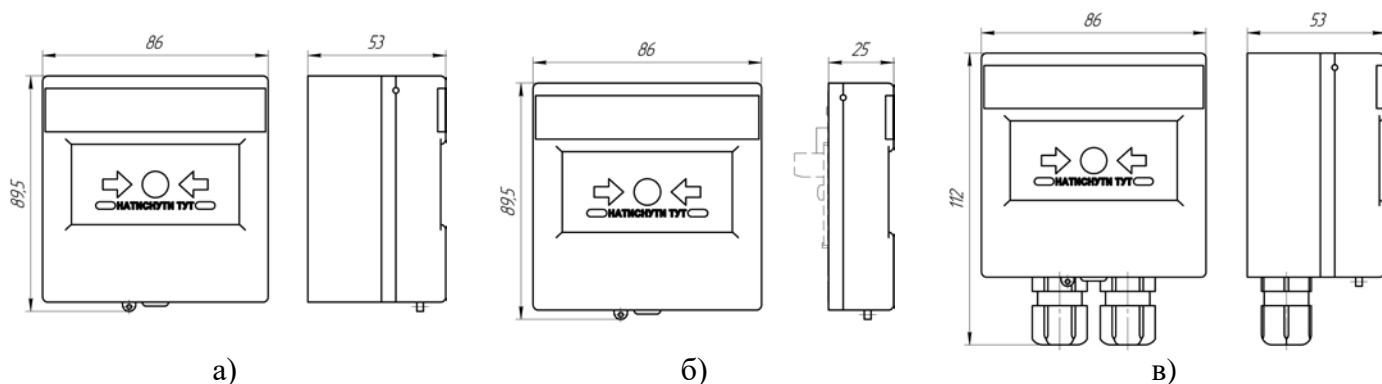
Внешний вид и габаритные размеры кнопок, размеры в мм.
